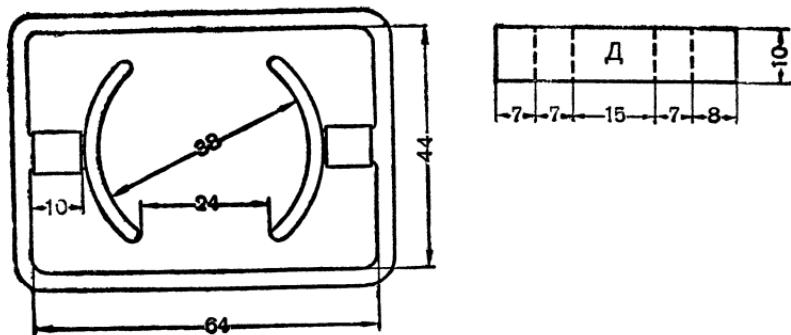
Детали статора № 6 (рис. 25). Наверху слева—схема сборки.
